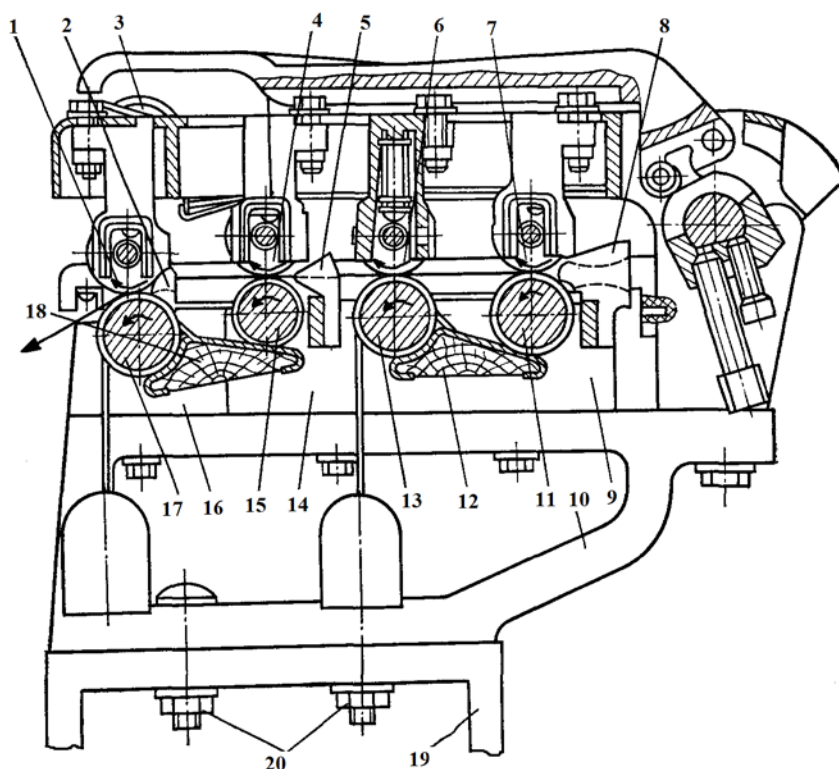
Четырехцилиндровый двухзонный вытяжной прибор с уплотнителями ленты и мычки
